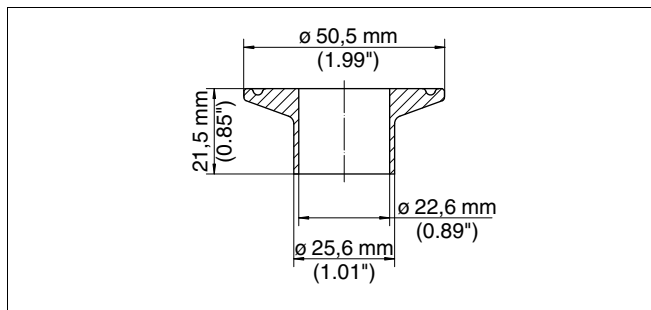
Medidas da luva soldada Clamp 1" PN16 DIN 32676, ISO 2852/316L
